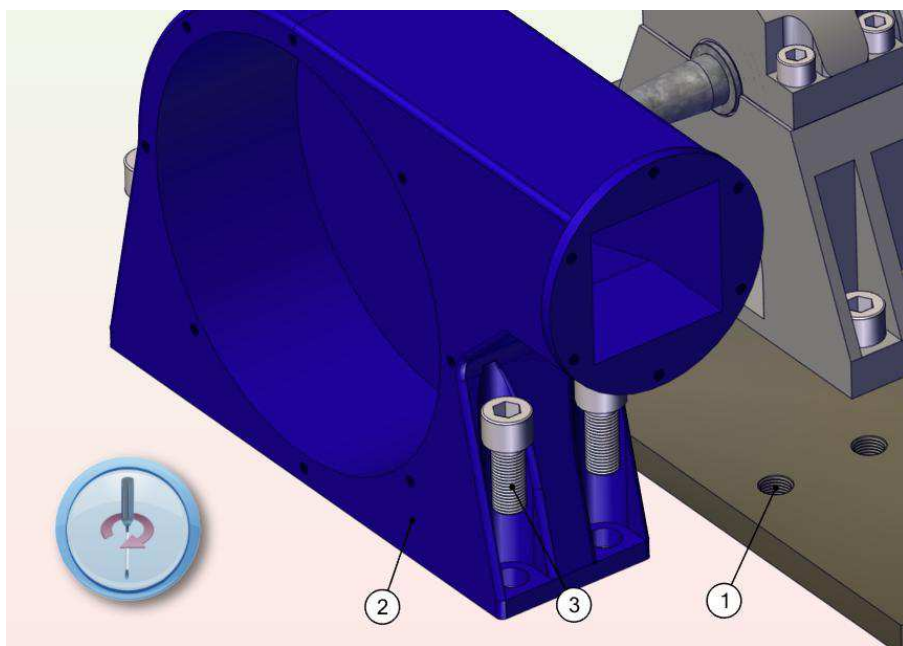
Схема встановлення корпусу вентилятора.
